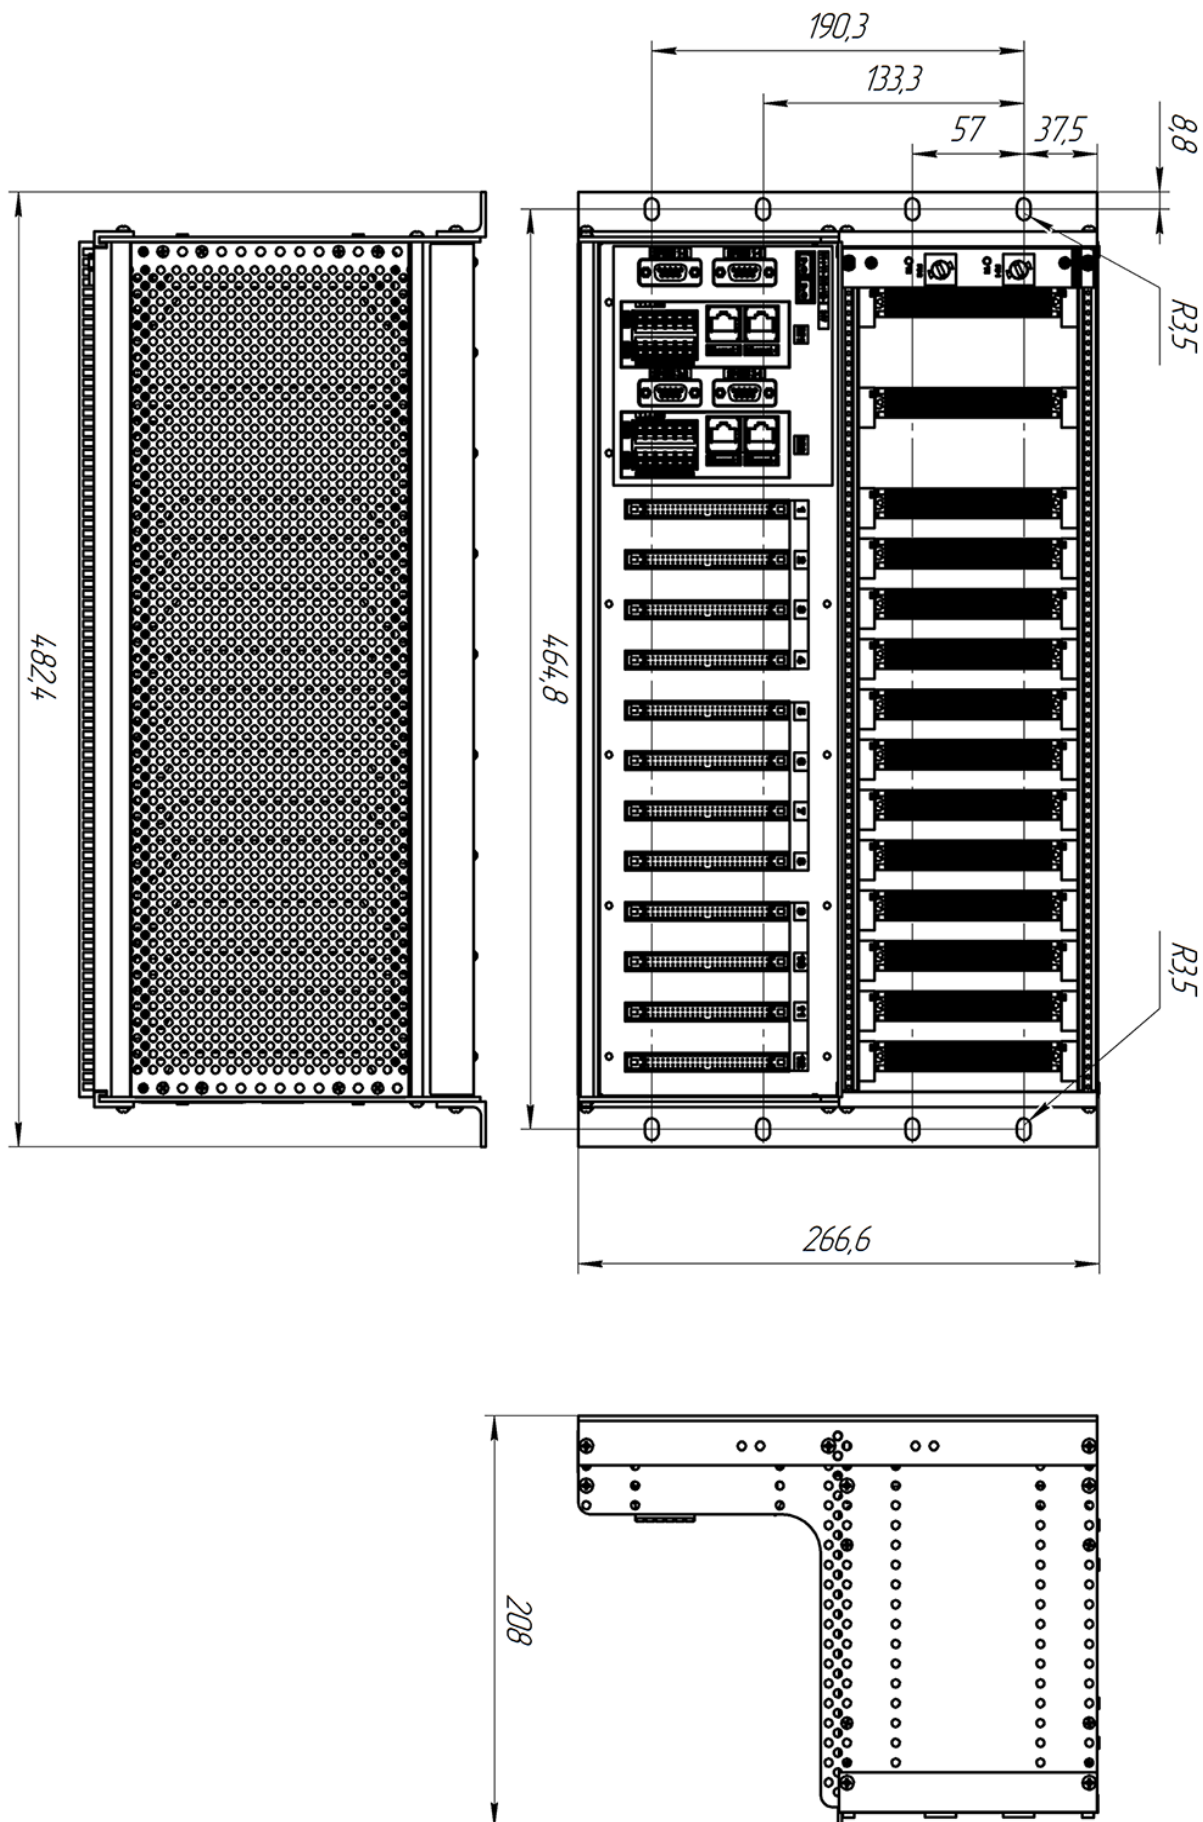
Чертеж общего вида каркаса CR6 MR с указанием габаритных размеров
